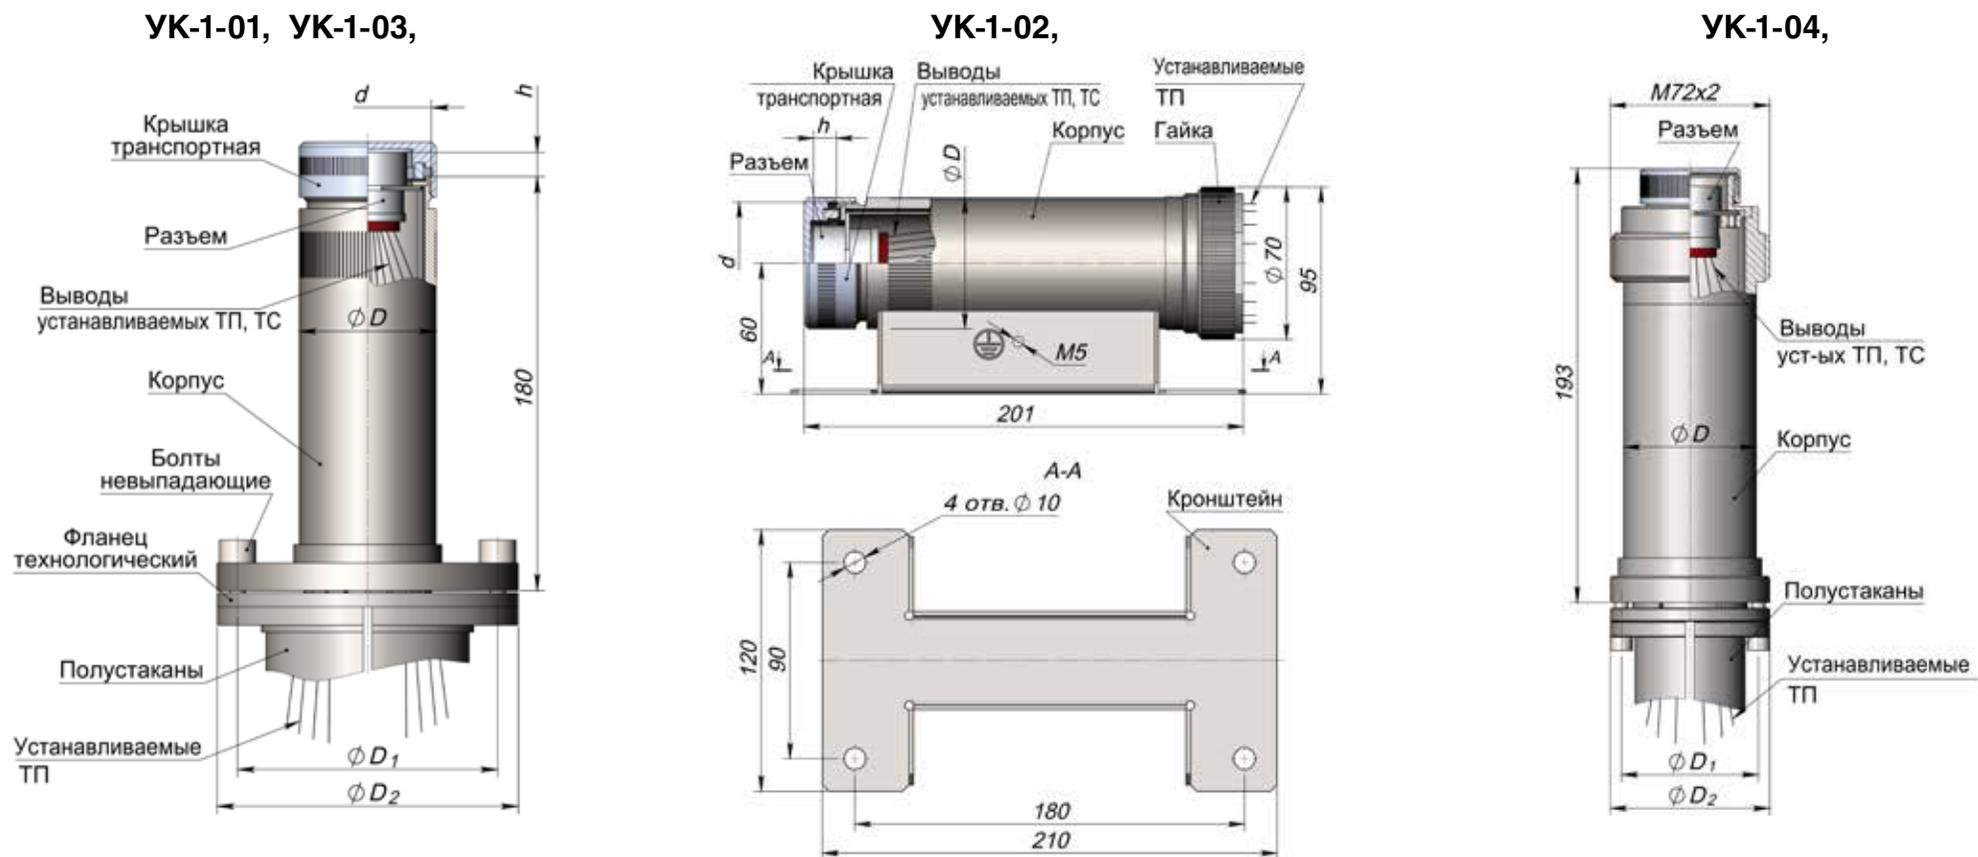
Габаритные и присоединительные размеры УК-1.
